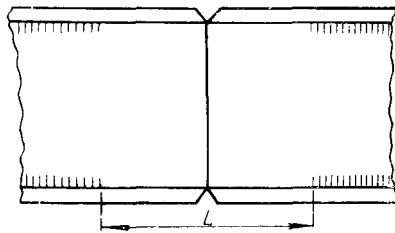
Собранный под сварку стык двутавровой балки
